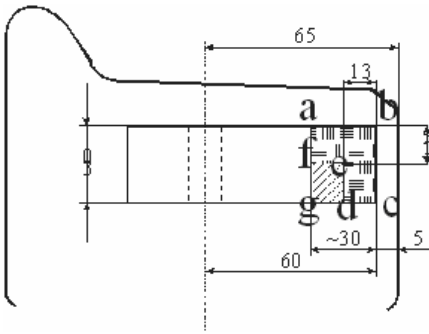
Схема вырезки образца для испытаний на вязкость разрушения
